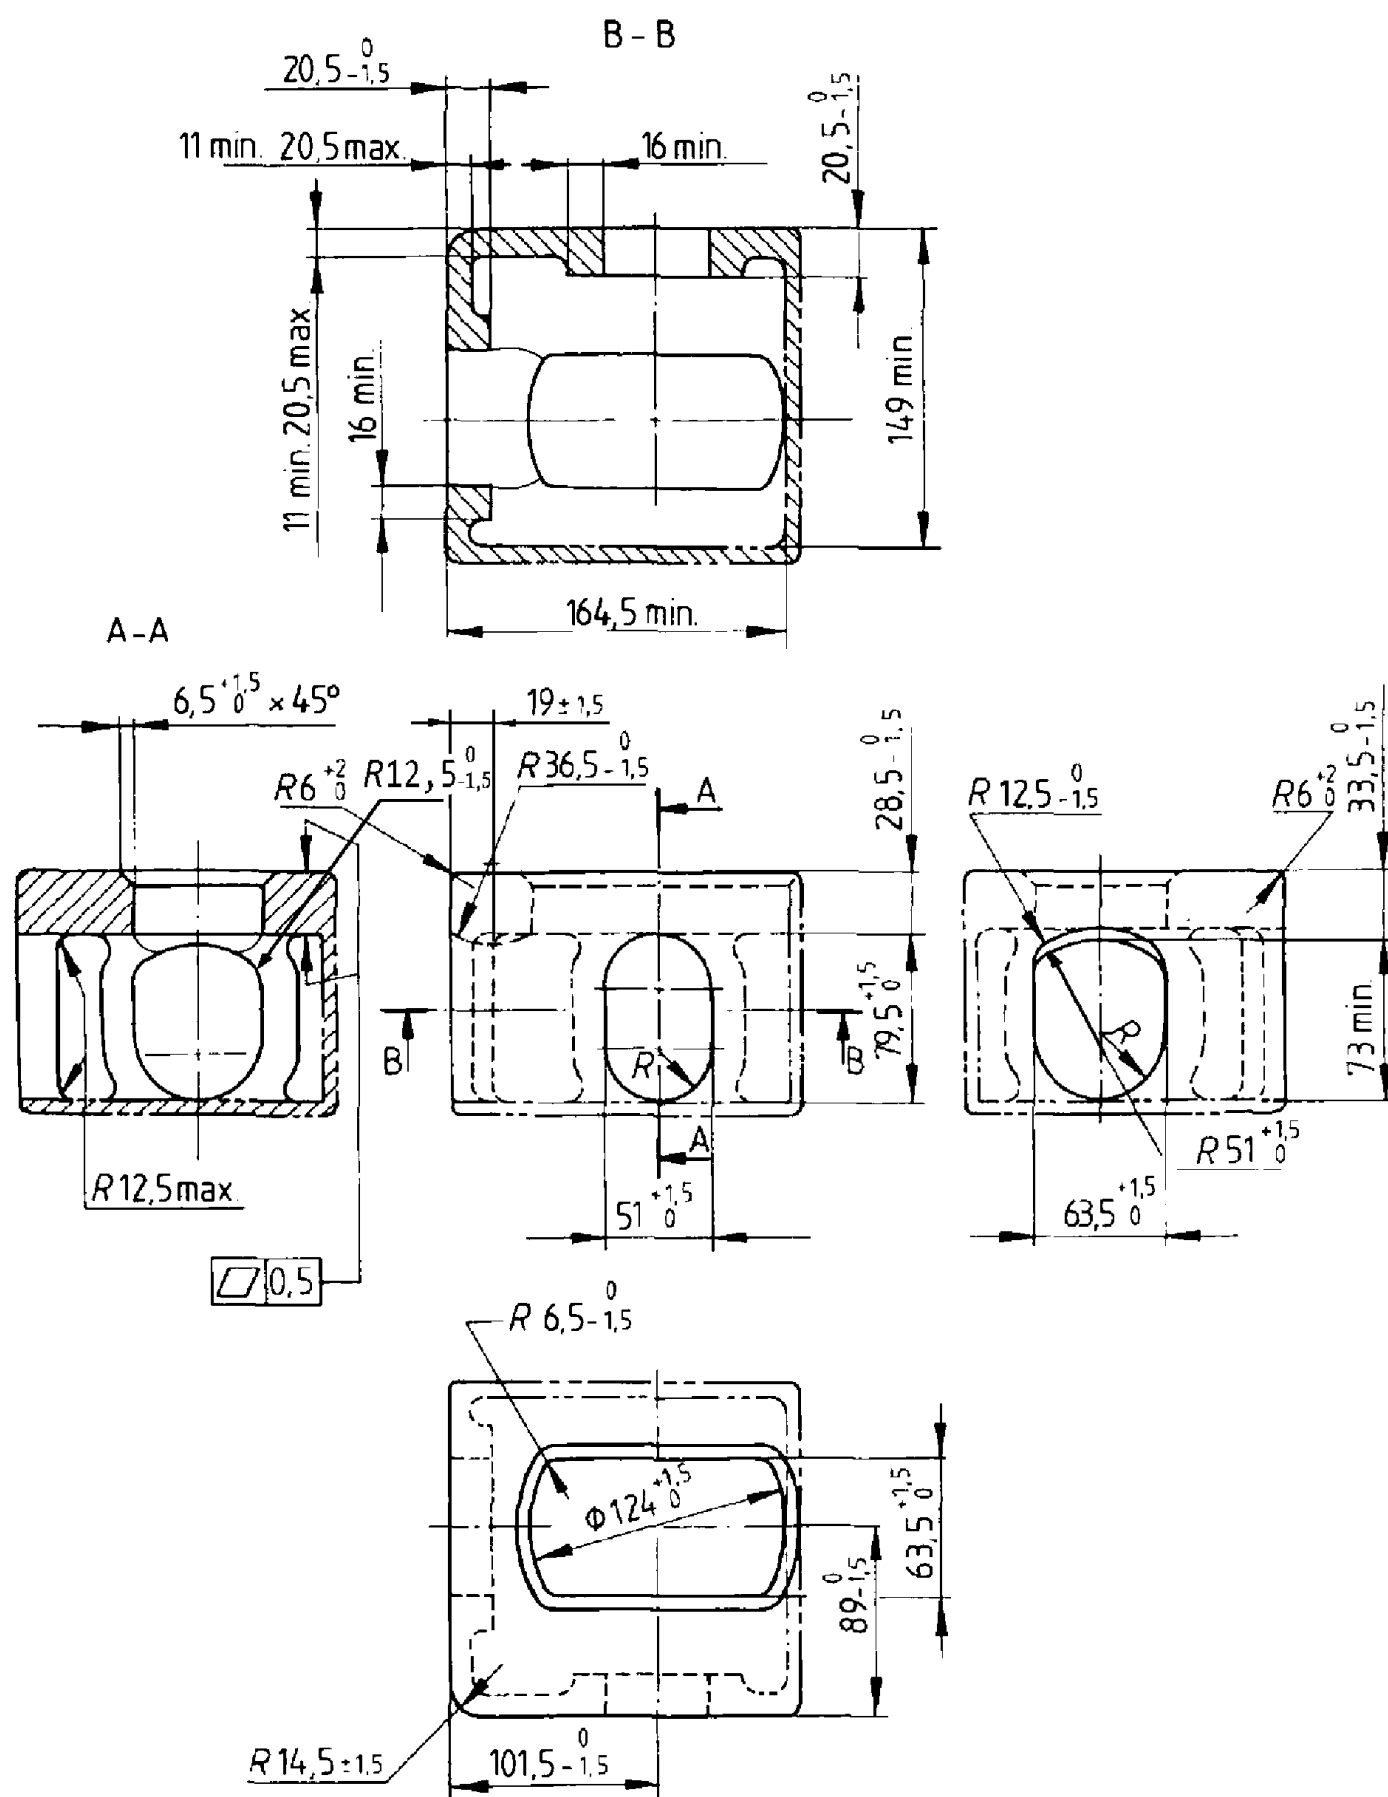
Верхний угловой фитинг, мм:
